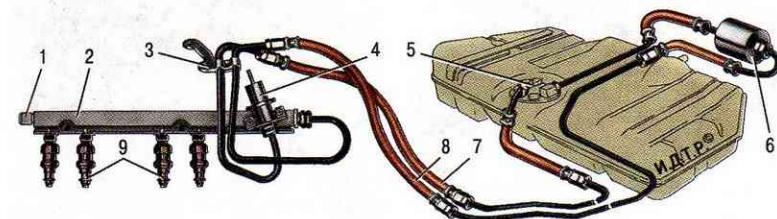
Система подачи топлива двигателей мод. 2111 и 2112: 1 — пробка штуцера для контроля давления топлива; 2 — рампа форсунок; 3 — скоба крепления топливных трубок; 4 — регулятор давления топлива; 5 — топливный насос; 6 — топливный фильтр; 7 — сливной топливопровод; 8 — подающий топливопровод; 9 — форсунки
